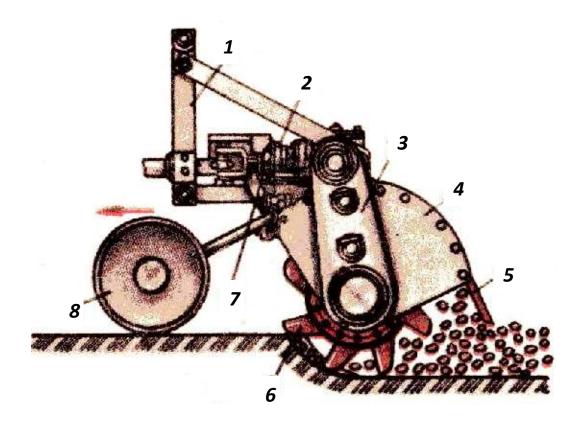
Почвообрабатывающая фреза ФБИ -2:
